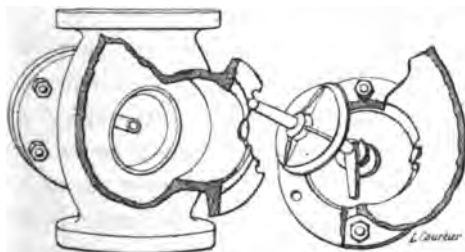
Rupture de la valve V de la chaudière n° 1 (Villefranche).
